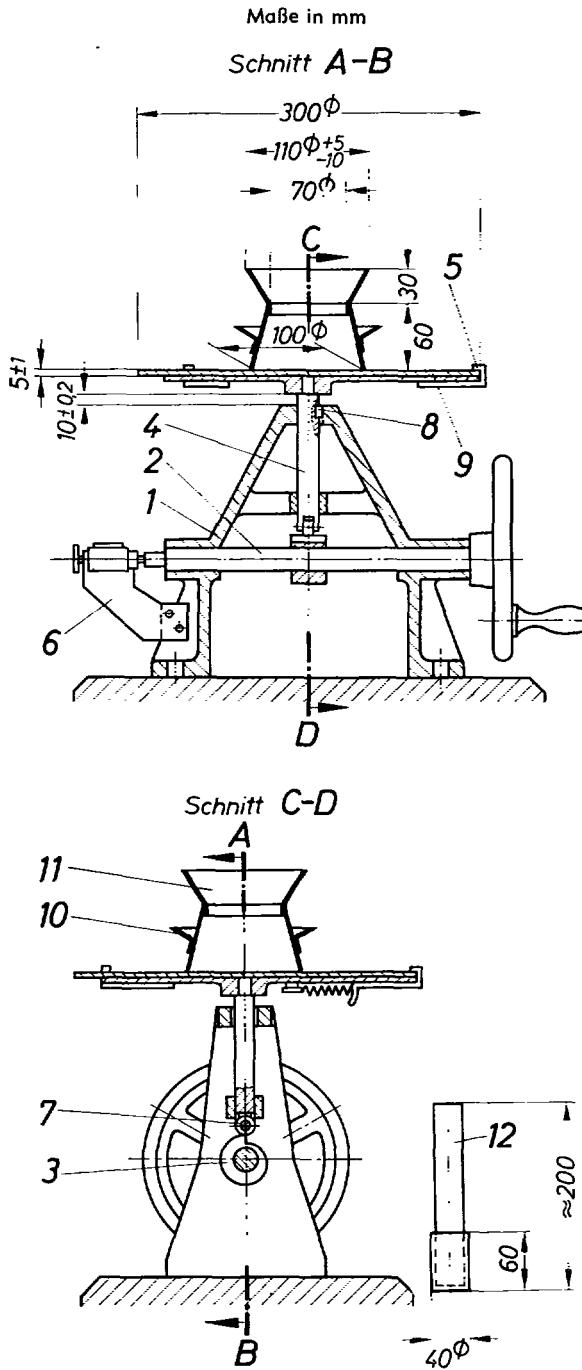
Rütteltisch und zugehöriger Stampfer (Bild rechts)
